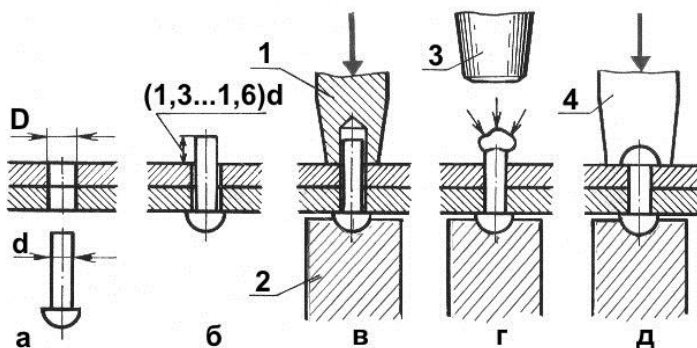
Этапы выполнения заклепочного соединения: а – сверление отверстий; б – размещение заклепки в отверстии; в – осаживание заготовок; г – расклепывание замыкающей головки; д – формирование замыкающей головки; 1 – натяжка; 2 – поддержка; 3 – молоток; 4 – обжимка
